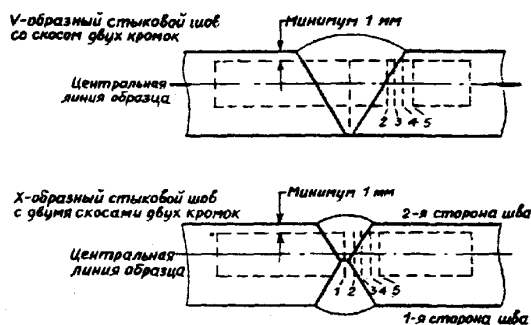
Ориентация образца для испытаний на ударный изгиб и образца с V-образным надрезом
